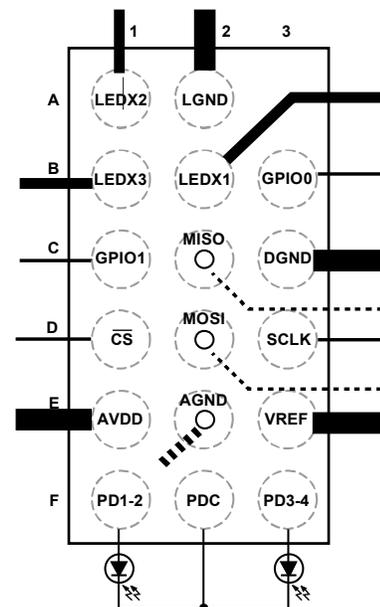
ADPD107 连接和 PCB 布局图，虚线自盲孔接出 (顶视图)
